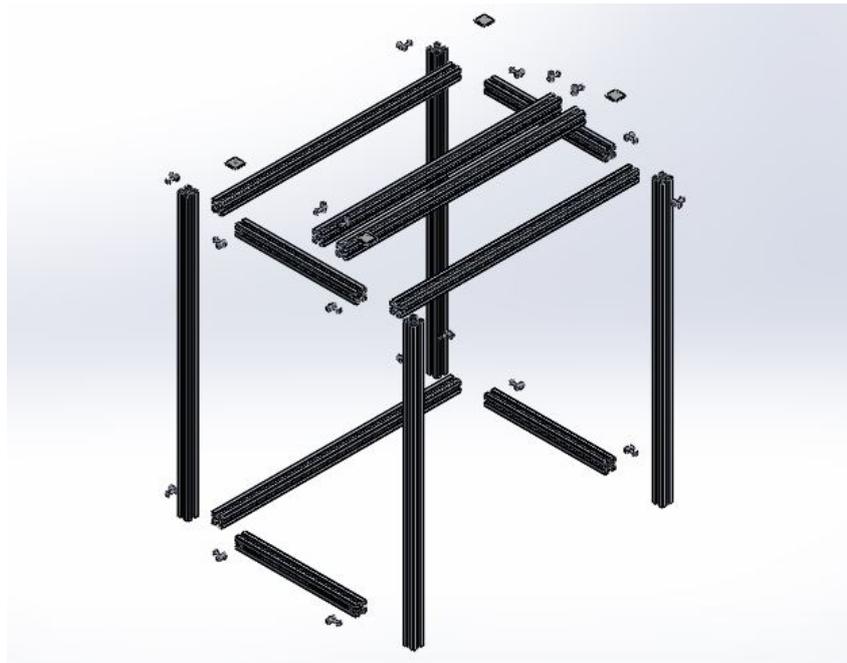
Estructura superior mesa de trabajo (Vista Explosionada)
